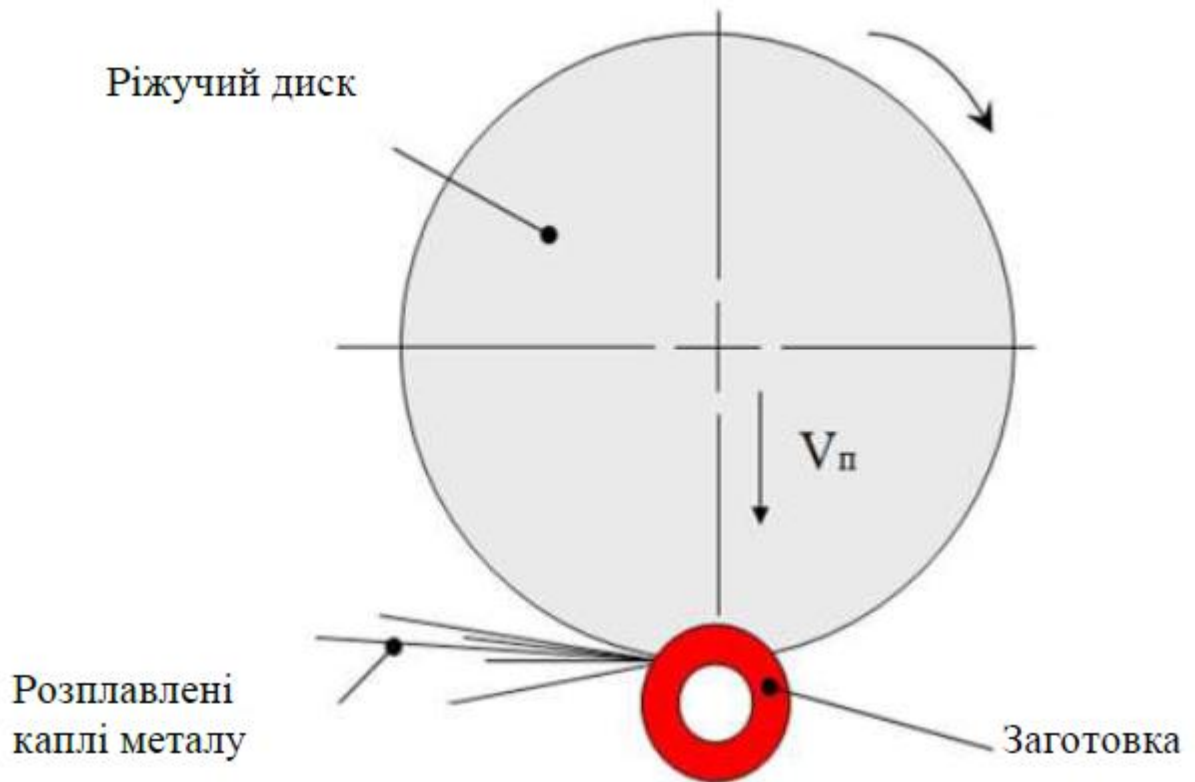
Схема термофрикційного різання заготовки: V_r – швидкість різання, V_p – швидкість подачі.
